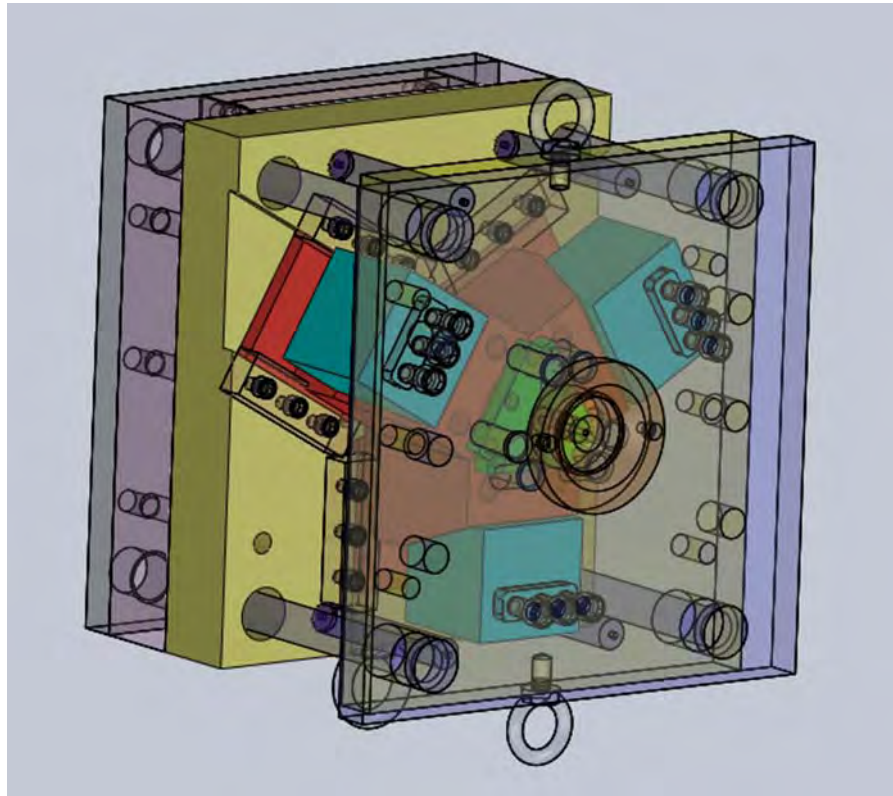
金型の組立図 (Assembled view of plastic injection mold).
